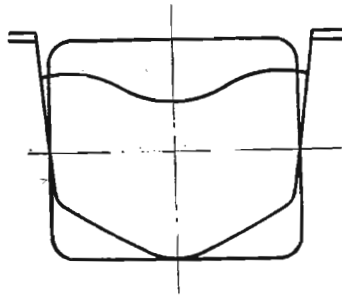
Обычный способ задачи квадратной заготовки в первый профильный калибр
